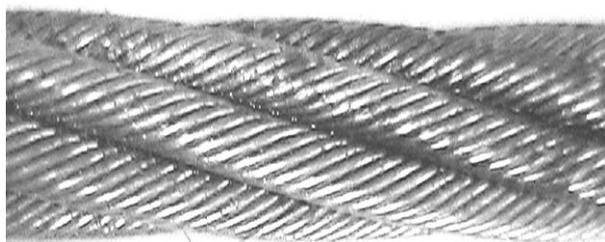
Образец № 4 каната двойной свивки диаметром изготовленный с равномерным натяжением прядей
